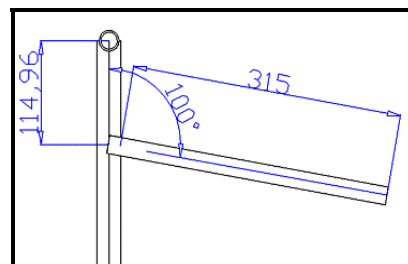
Posição de soldagem do metalon (Figura 2.26).
